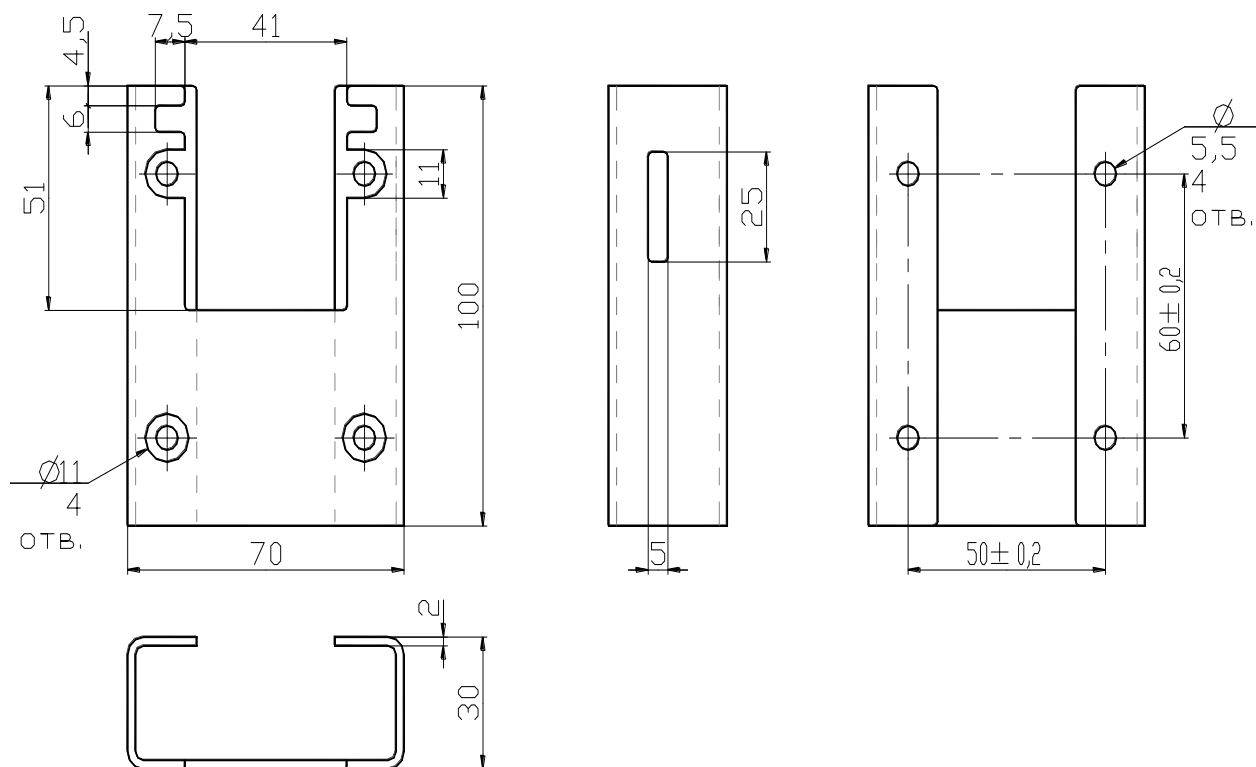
Габаритные и установочные размеры кронштейна M12.021.09.001
